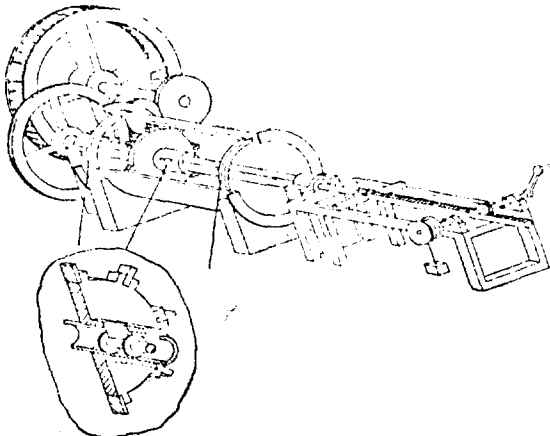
Wilkinson의 Boring machine 中心을 고정 한 칼
